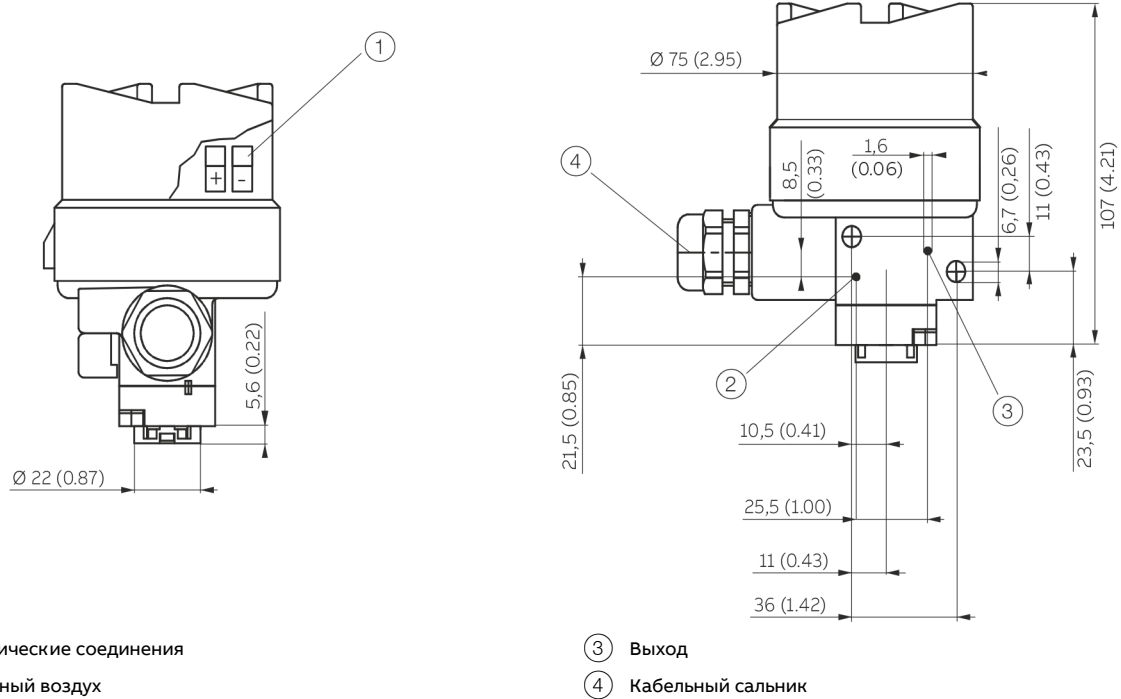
Габаритные размеры конструкции полевого корпуса для настенного монтажа или монтажа на трубе
